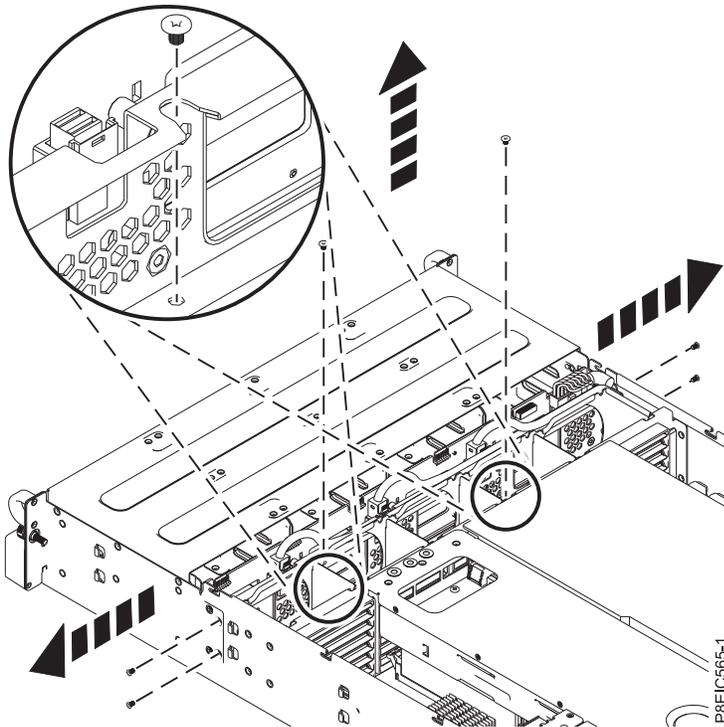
Schrauben an der Rückwandplatine des Laufwerks entfernen
